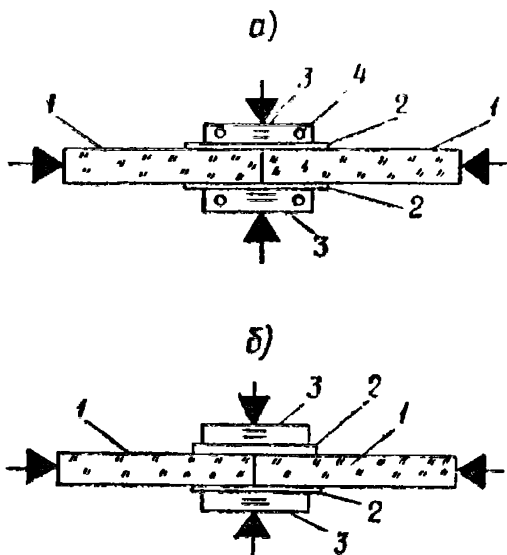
Схема приспособления для сварки оргстекла встык прессованием:
